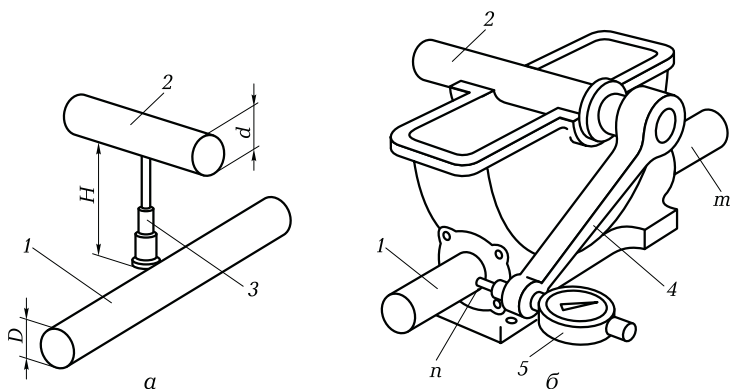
Схемы контроля расположения осей отверстий в корпусе червячного редуктора:
